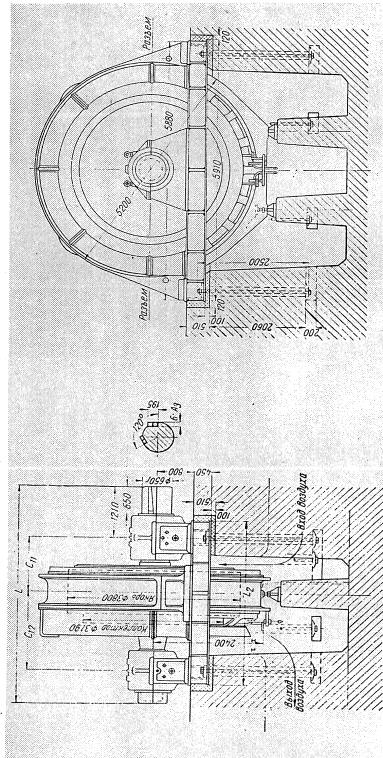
Размеры зениторвательных ПУК 38055, ПУК 38065 и ПУК 38080 для безшарнирных шахтных подъемников.
